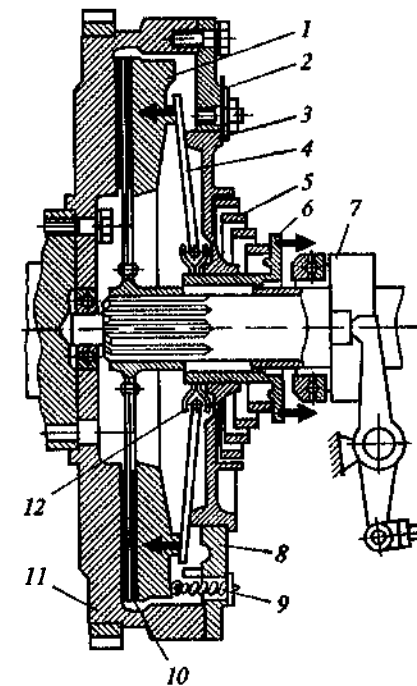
Однодисковое сцепление с конической пружиной грузового автомобиля:
